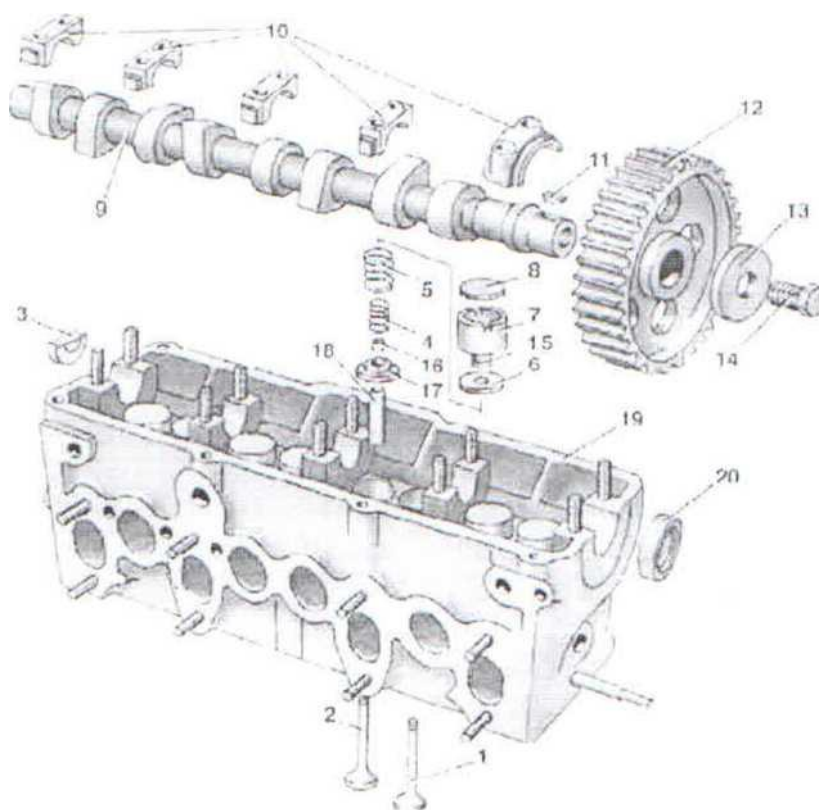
Головка блока цилиндров, распределительный вал и клапаны
